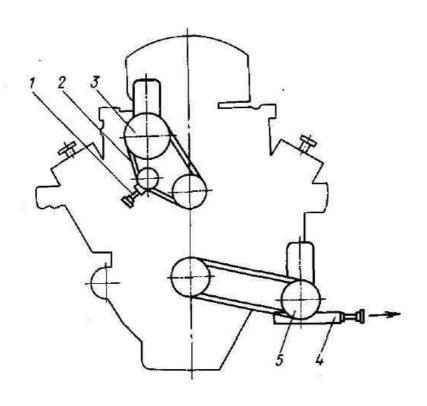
Привод компрессоров: 1,4 - натяжное устройство; 2 - ремень клиновой; 3,5 - компрессоры
